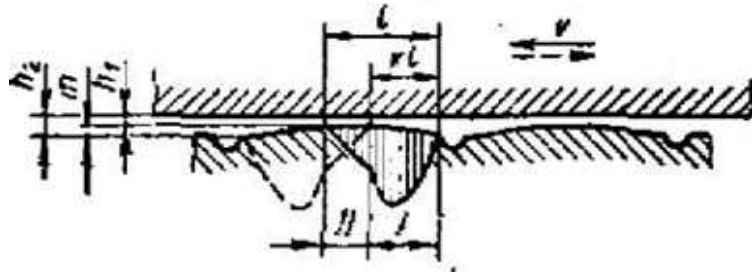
Ділянка зубчастих поверхонь шестерні з гідродинамічними кишеньками і зубчастого колеса, що сполучається
